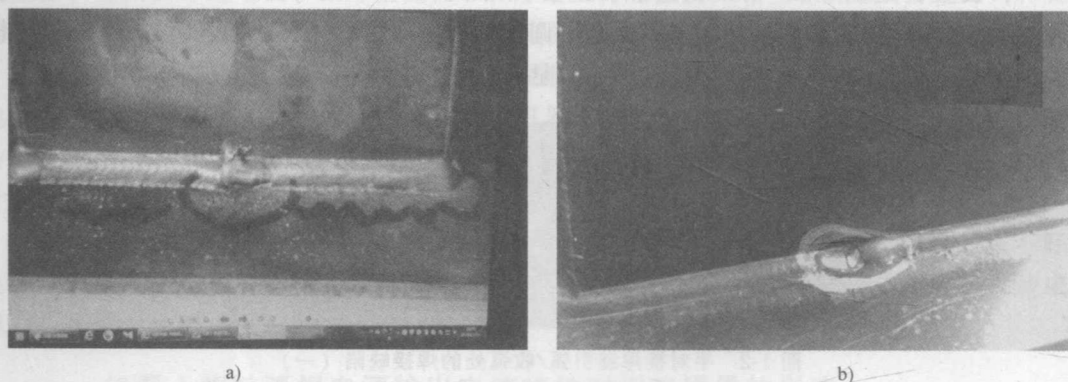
T形接头角焊缝引弧/收弧处的焊接缺陷
